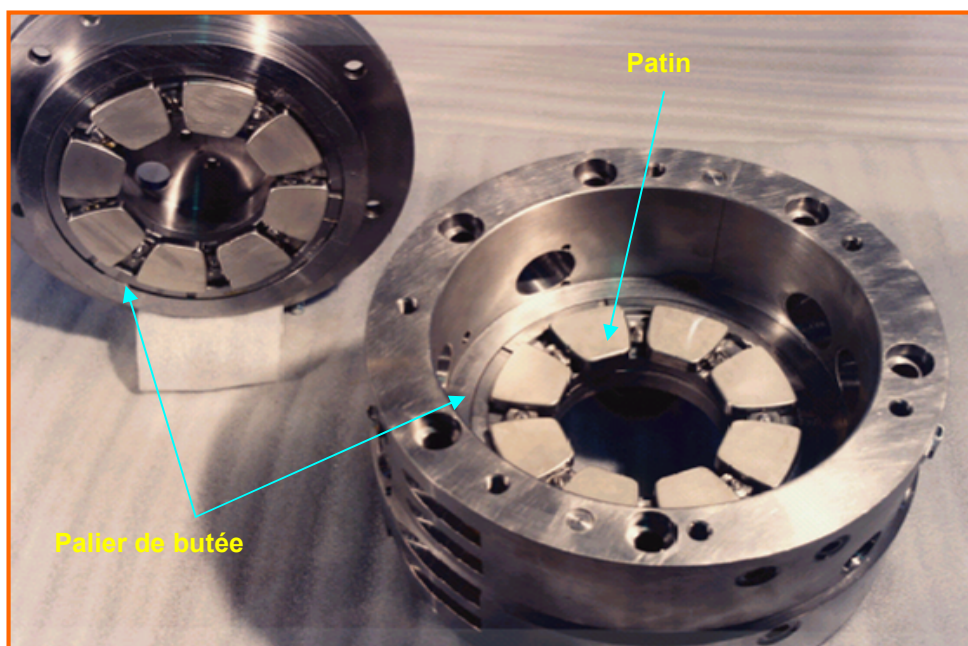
Palier de butée du compresseur BCL 606-3/A.
